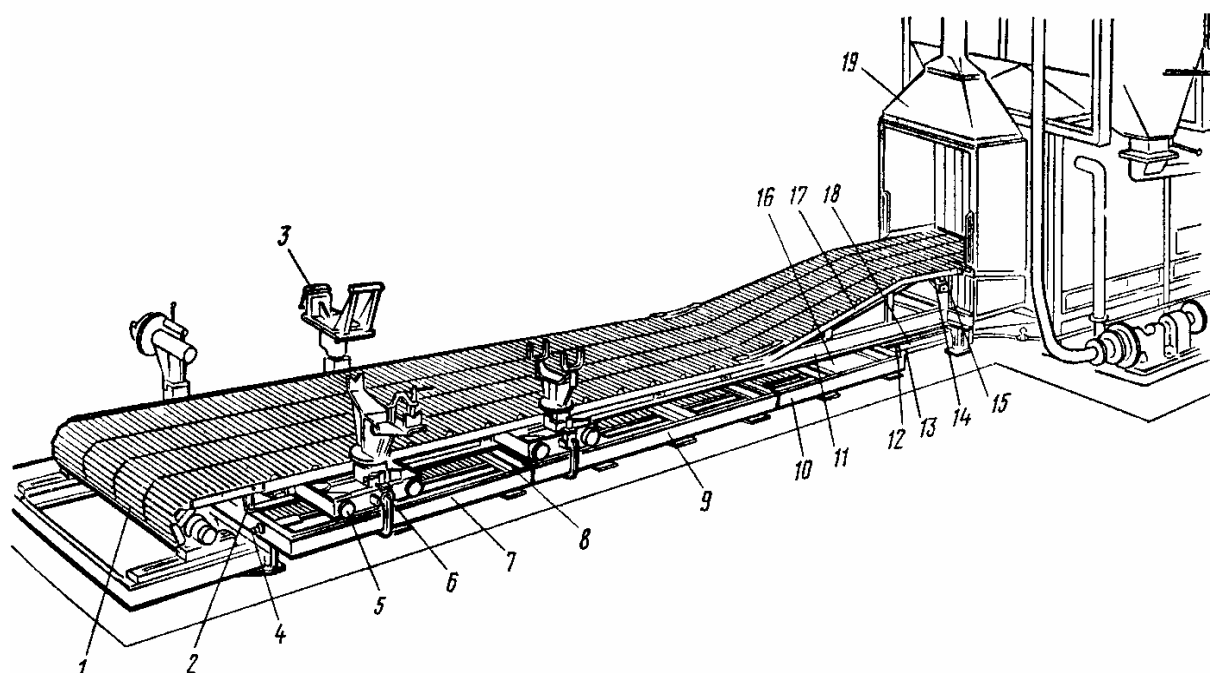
Конвейер с пластинчатым транспортером для разборки автомобильных агрегатов: 1 – транспортер; 2 и 12 – упоры; 3 – разборочный поворотный стенд; 4 – натяжное устройство; 5 – тележка; 6 – винтовой зажим; 7 – рама; 8, 11, 17 и 18 – направляющие; 9 и 10 – секции; 13 – патрубок; 14 и 15 – конечные выключатели; 16 – поддон; 19 – очистная струйная машина
